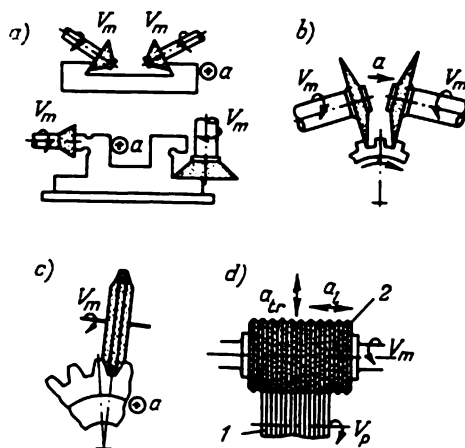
Principaux procédés de rectification des surfaces de forme, des engrenages et des filetages
